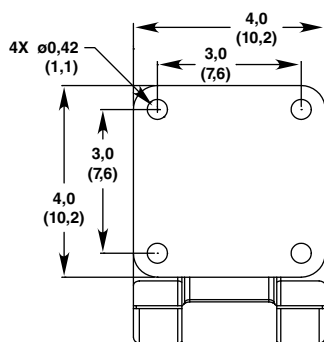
Dimensiones del soporte de montaje Q9033 en pulgadas (cm)
